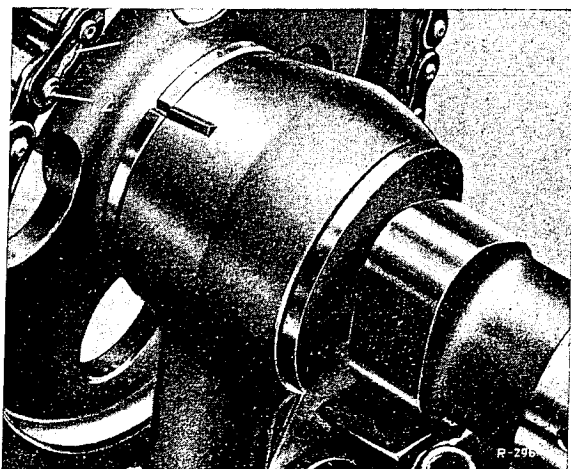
Die Strichmarken auf der Ausgleichsscheibe und dem Nockenwellenlager sind gefluchtet
